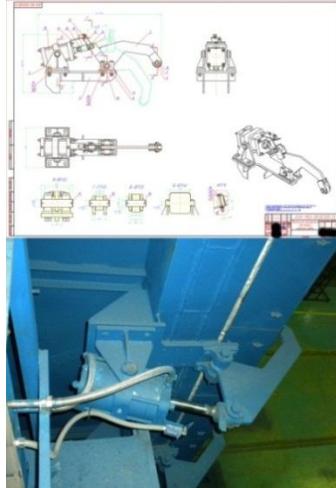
Сборочный чертеж и фотография АНХ-М63-08.00.000 СБ Механизм прижатия заслонки
